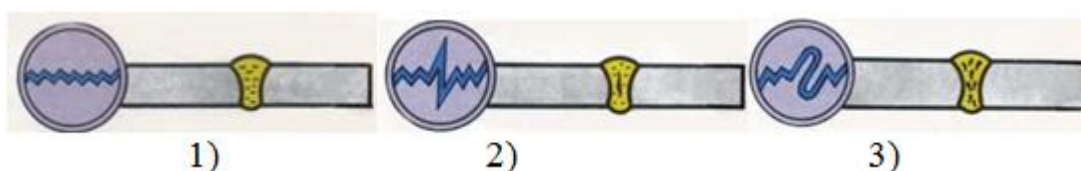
Схема ультразвукового контроля стыкового шва
